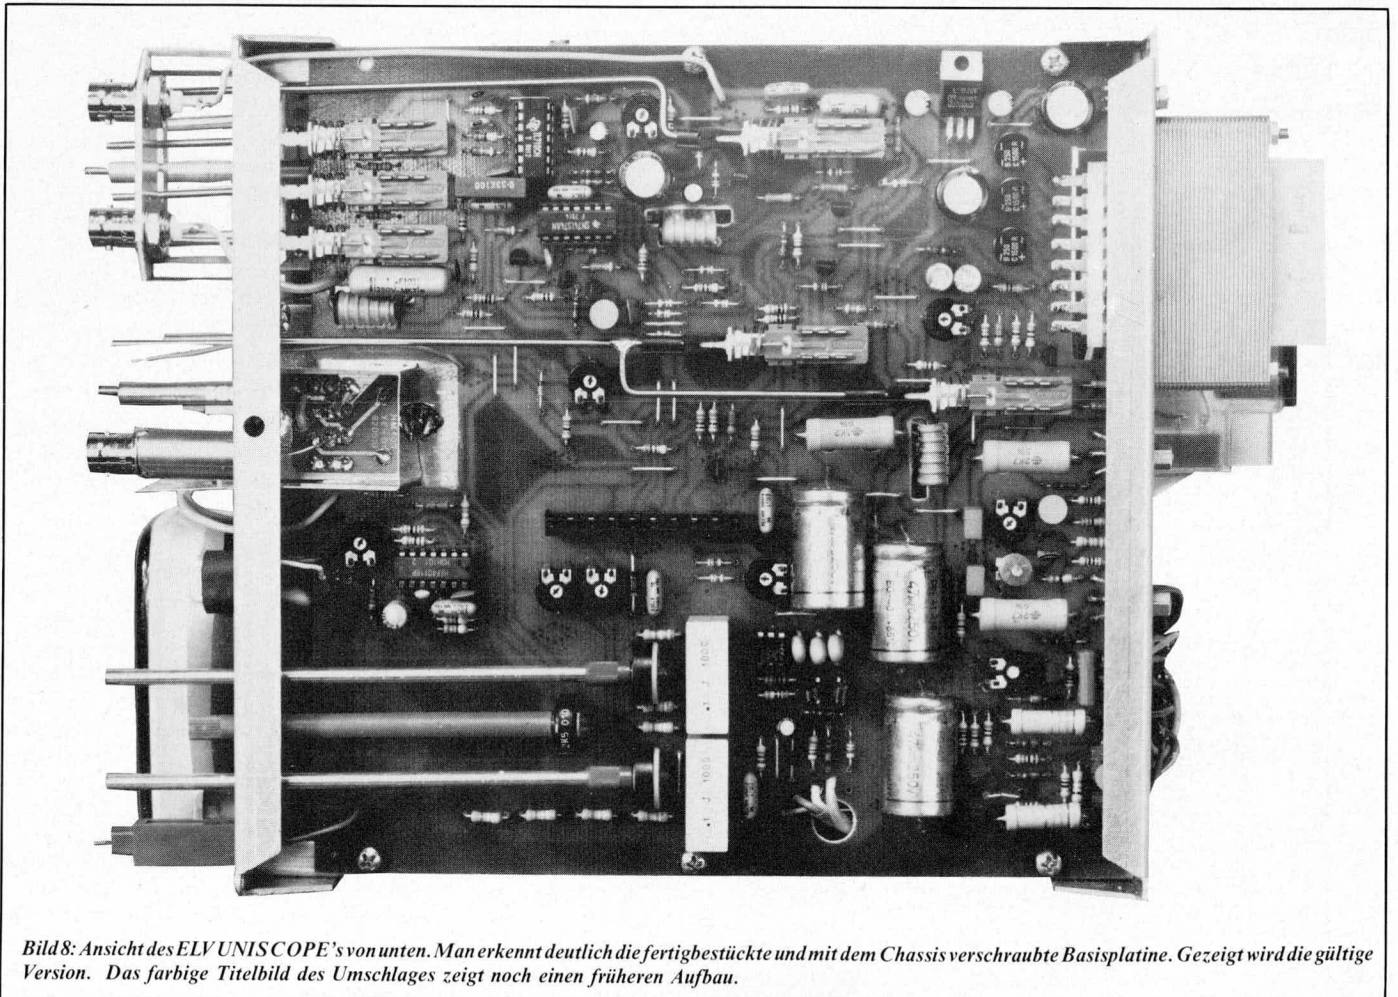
Ansicht des ELV UNISCOPE's von unten. Man erkennt deutlich die fertigbestückte und mit dem Chassis verschraubte Basisplatine. Gezeigt wird die gültige Version. Das farbige Titelbild des Umschlages zeigt noch einen früheren Aufbau.
